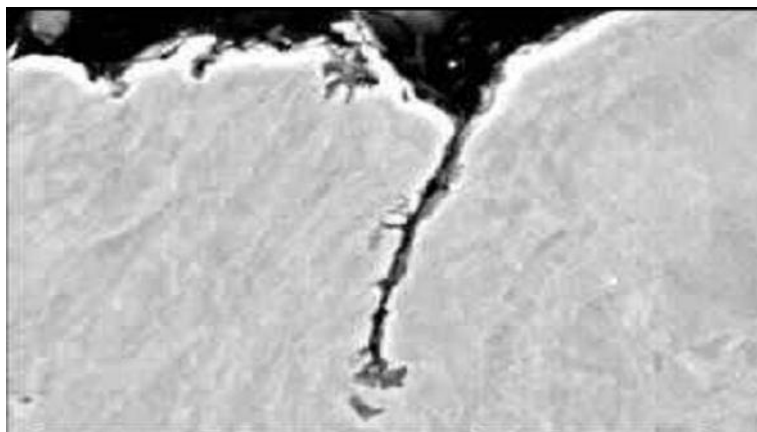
Fissure dans des joints soudés [9]
